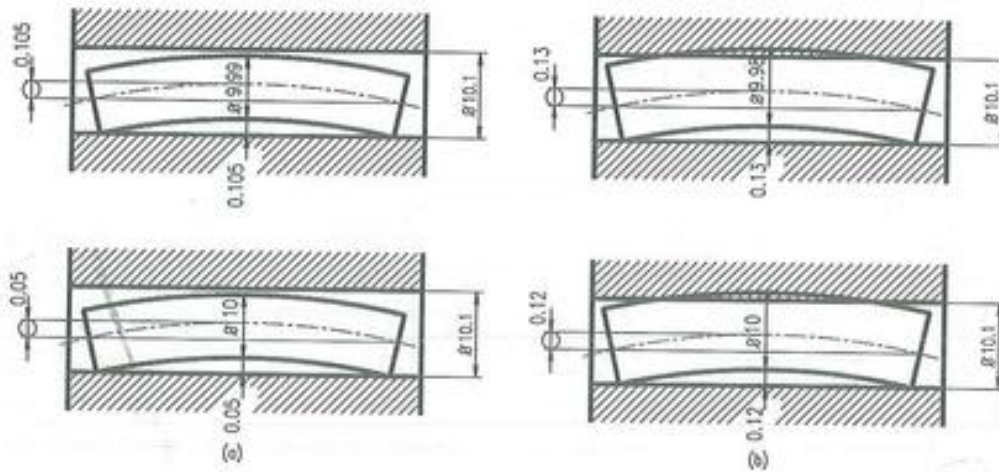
(a) Piezas que cumplen con las tolerancias especificadas. (b) Piezas que cumplen con la tolerancia dimensional pero no con la geométrica.
